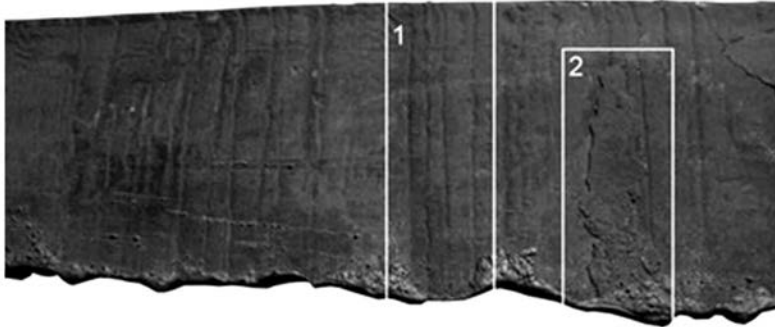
Розташування складок (1) і «залікована» після прориву корки в кристалізаторі ділянка заготовки (2).
